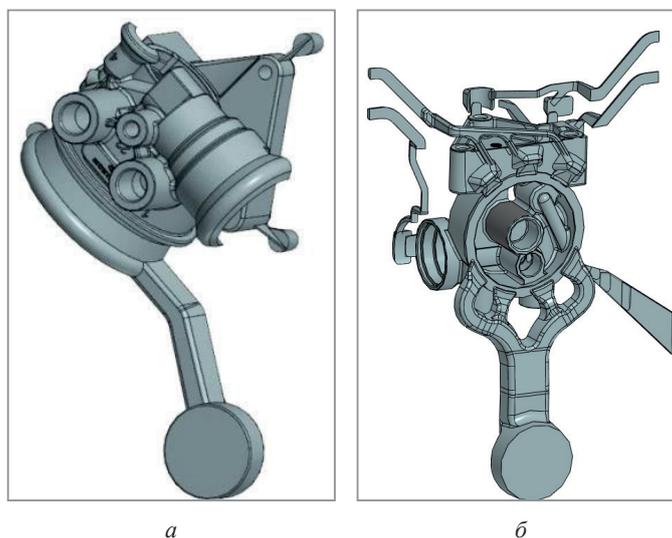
3D-модель отливки «Корпус» с литниковой системой с применением пресс-формы: *а* – серийной конструкции; *б* – экспериментальной с усовершенствованной конструкцией литниковой и вентиляционной системы
